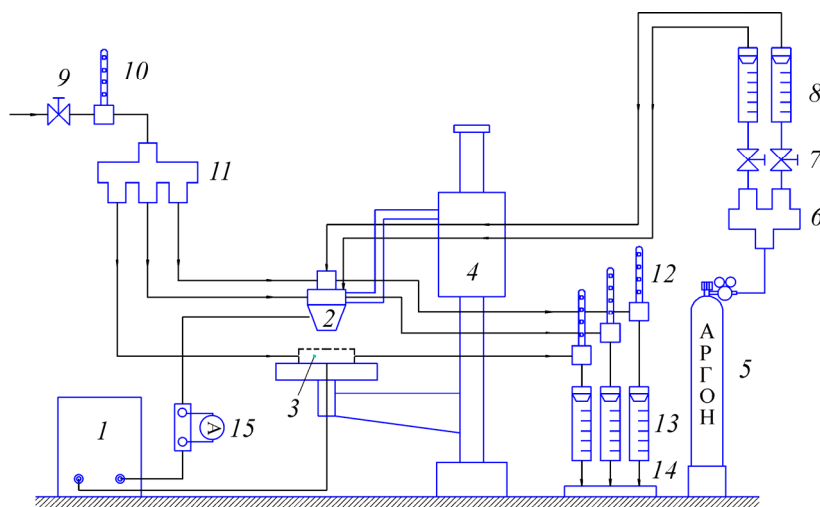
Плазменная установка: 1 – источник питания; 2 – плазмотрон; 3 – изделие; 4 – сварочный манипулятор; 5 – баллон с аргонem; 6 – коллектор газовый; 7 – вентиль газовый; 8 – ротаметр газовый; 9 – вентиль водяной; 10, 12 – термометр ртутный; 11 – коллектор водяной; 13 – ротаметр водяной; 14 – слив; 15 – амперметр
